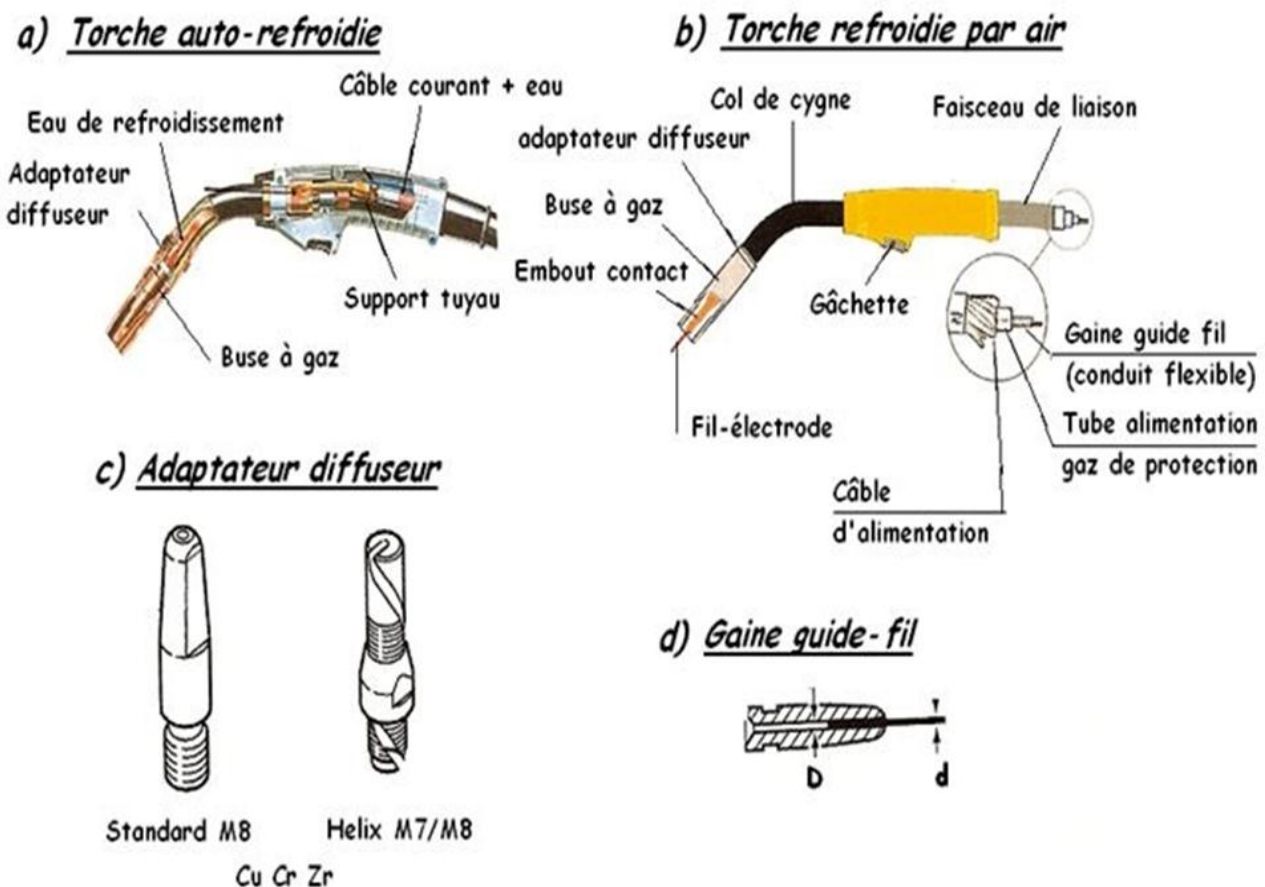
La torche de soudage Mig-Mag.
